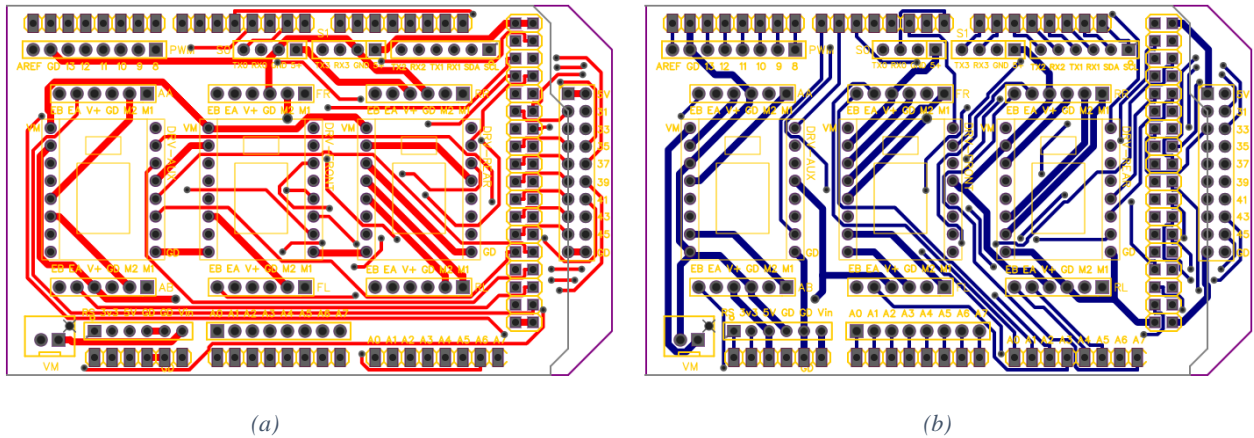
(a) Ruteado de la capa superior de la PCB, (b) Ruteado de la capa inferior de la PCB
